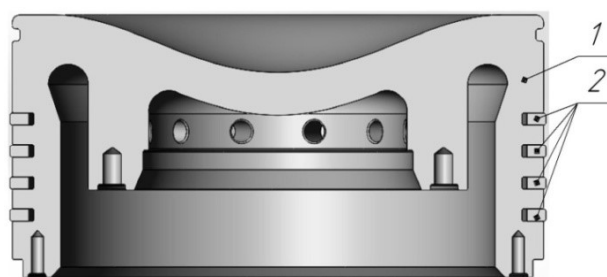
Сборка головки поршня судового МОД типа L35MC и колец:
